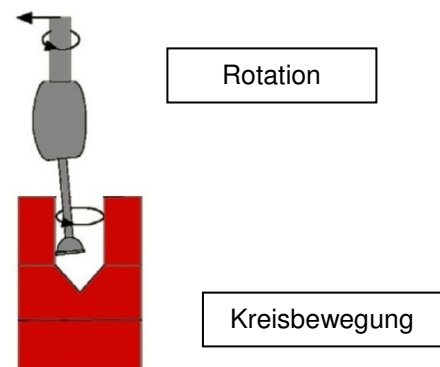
Das Werkzeug ins Zentrum der zweiten Bohrung bewegen. Rotation und Kreisbewegung des Werkzeugs stoppen.
